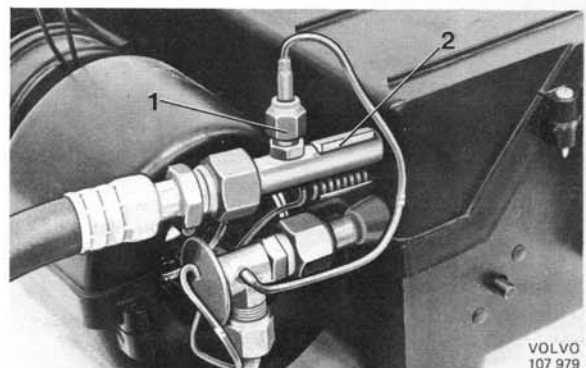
Ausbau des thermischen Expansionsventils, früh. Ausf.
